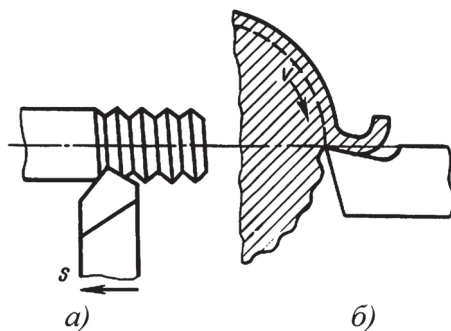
Образование шероховатости поверхности при токарной обработке:
